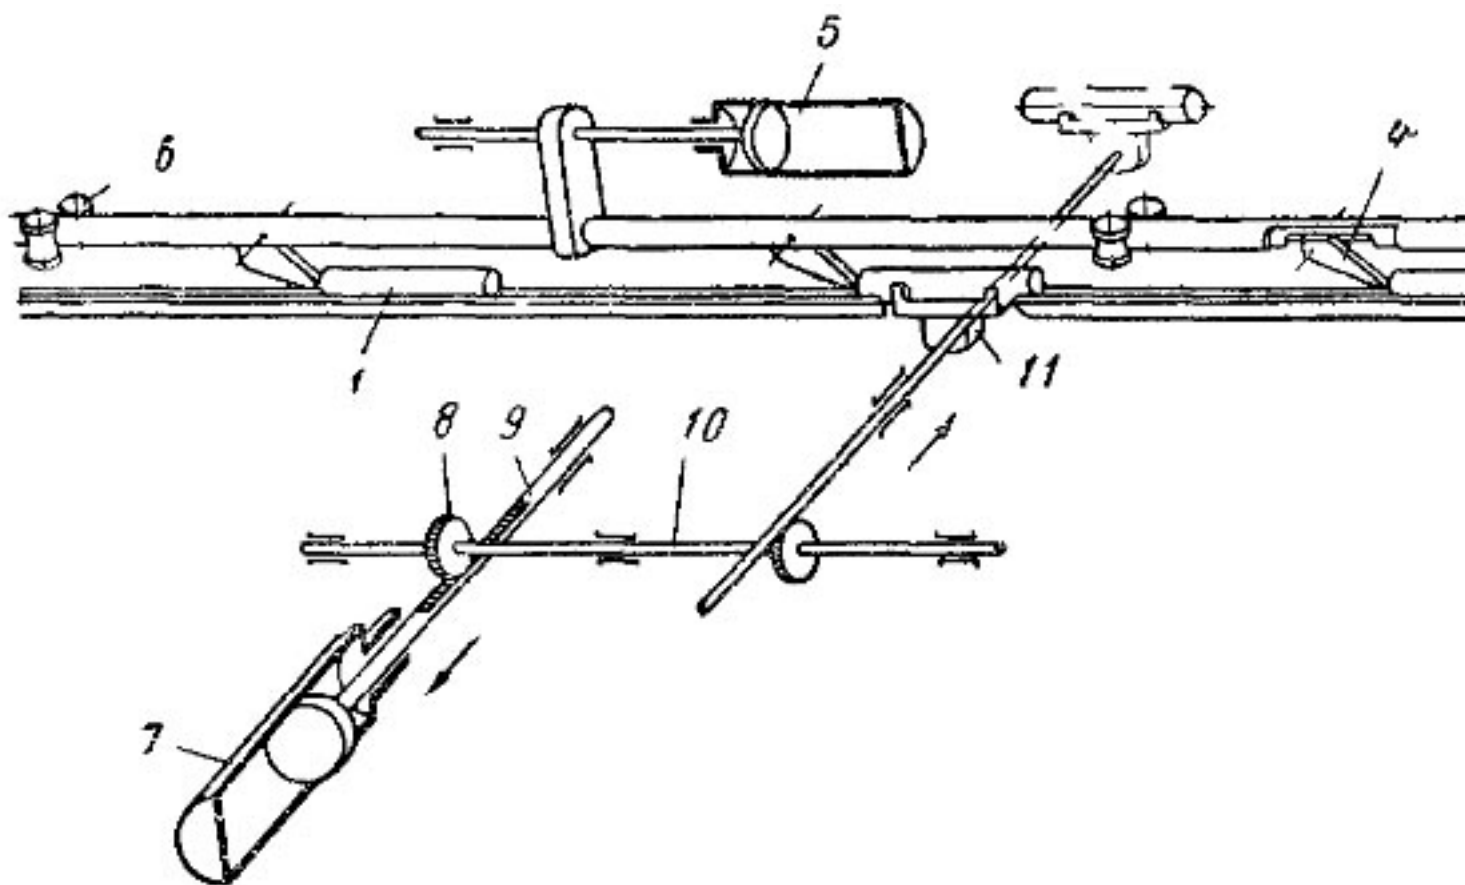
Схема транспортного устройства автоматической линии для обработки ступенчатых валов
